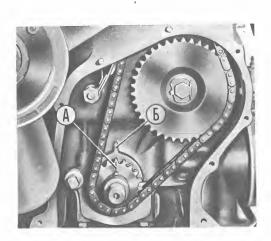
Установка ведущей звездочки цепного привода: А и Б — контрольные метки.
